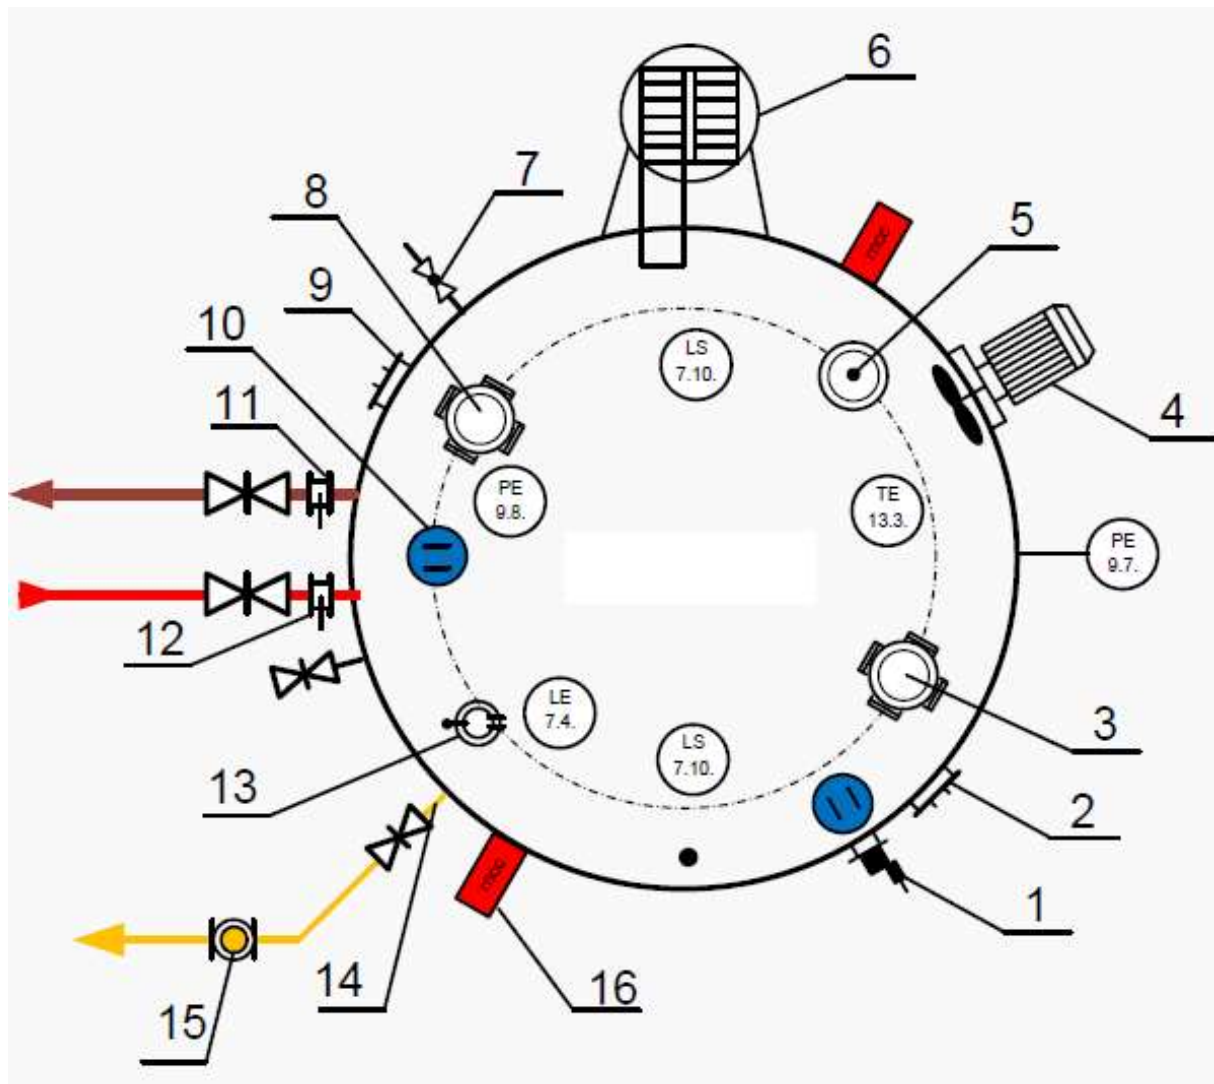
Схема расположения оборудования и приборов КИП:
